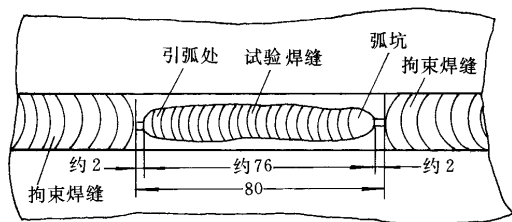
采用焊条自动送进装置焊接时试验焊缝位置
